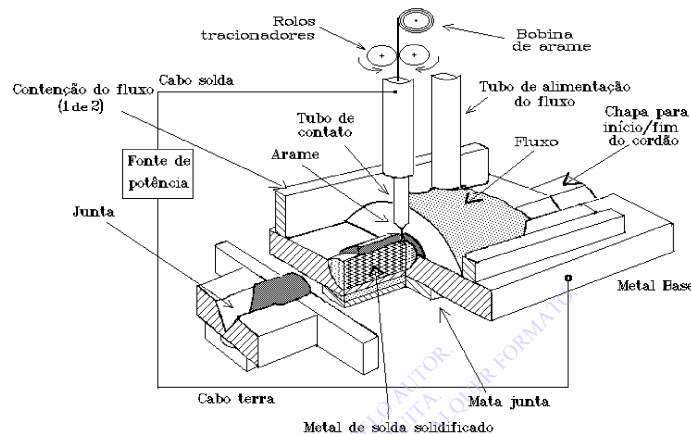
Equipamentos e acessórios (cabecote) Básicos para a Soldagem por Arco Submerso.
